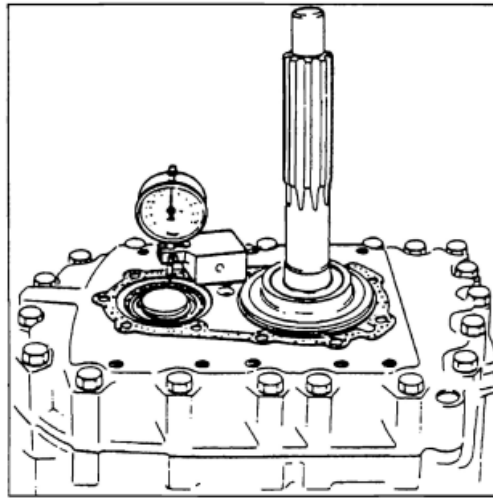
Вимірювання осадки зовнішньої обойми переднього роликотідшипника проміжного вала.
